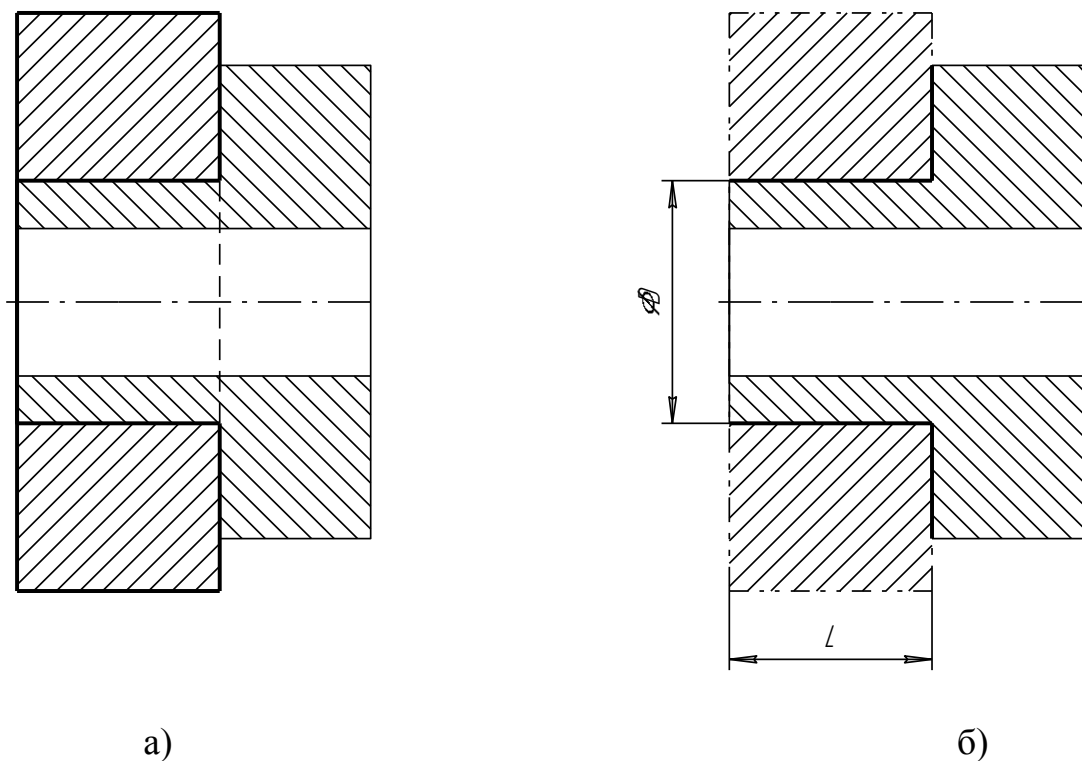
Пример выполнения чертежа привариваемой детали
